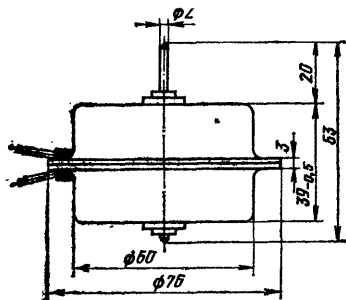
Габаритный чертеж электродвигателя ТСК-1.
